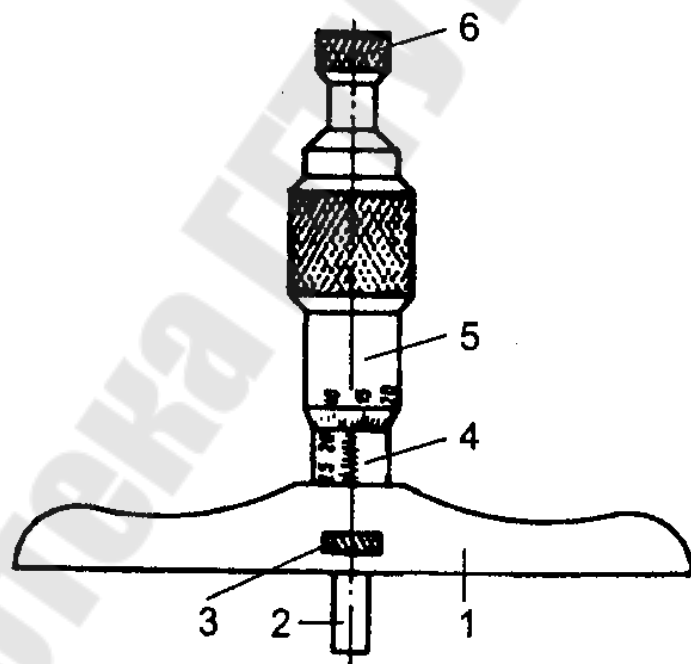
Микрометрический глубиномер: 1 – корпус; 2 – микрометрический винт; 3 – стопор; 4 – стержень; 5 – барабан; 6 храповой механизм.
